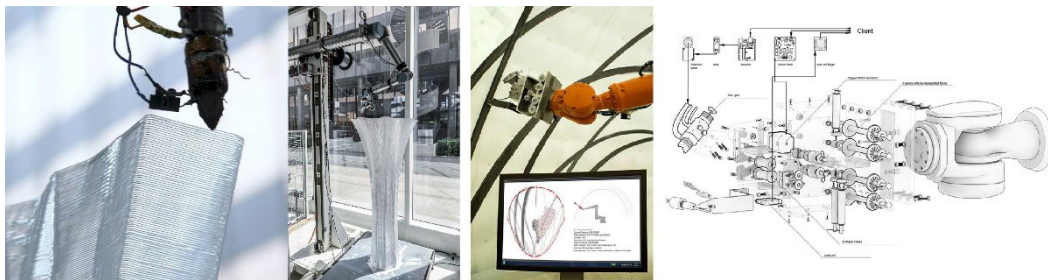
Adaptação do braço robótico – pavilhão ICD/ITKE e Future Tree
